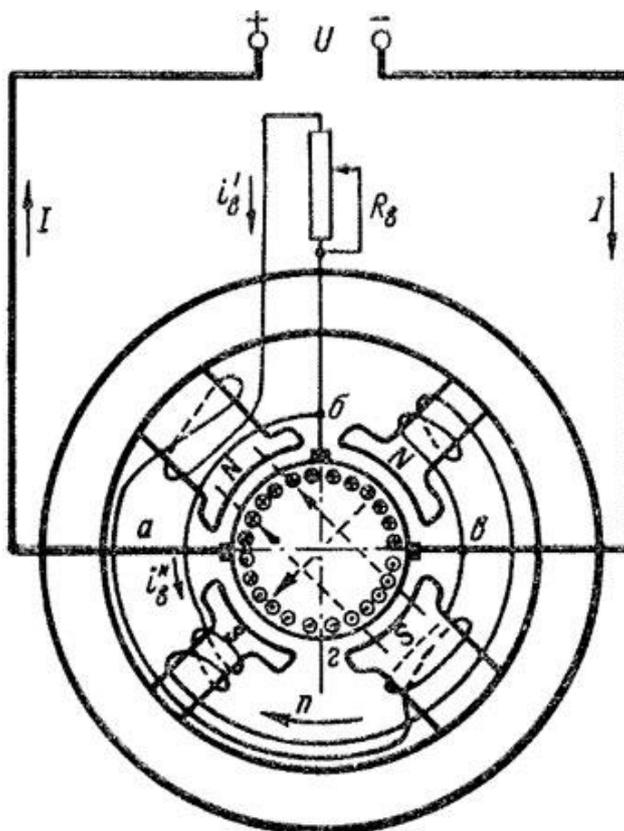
Сварочный генератор с расщепленными полюсами
